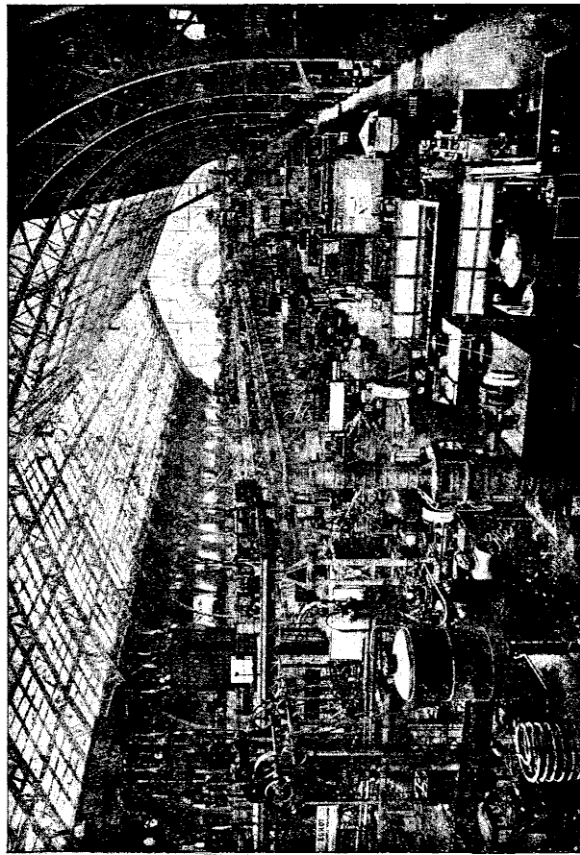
Vue intérieure avec les Machines en Mouvement.
